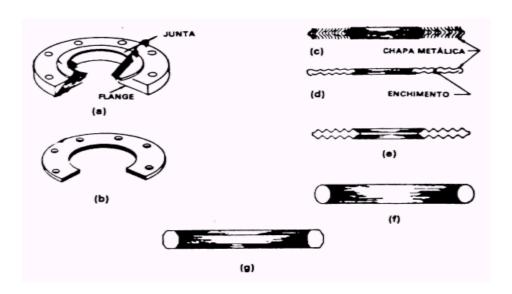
Tipos de Juntas para as Conexões Flangeadas
